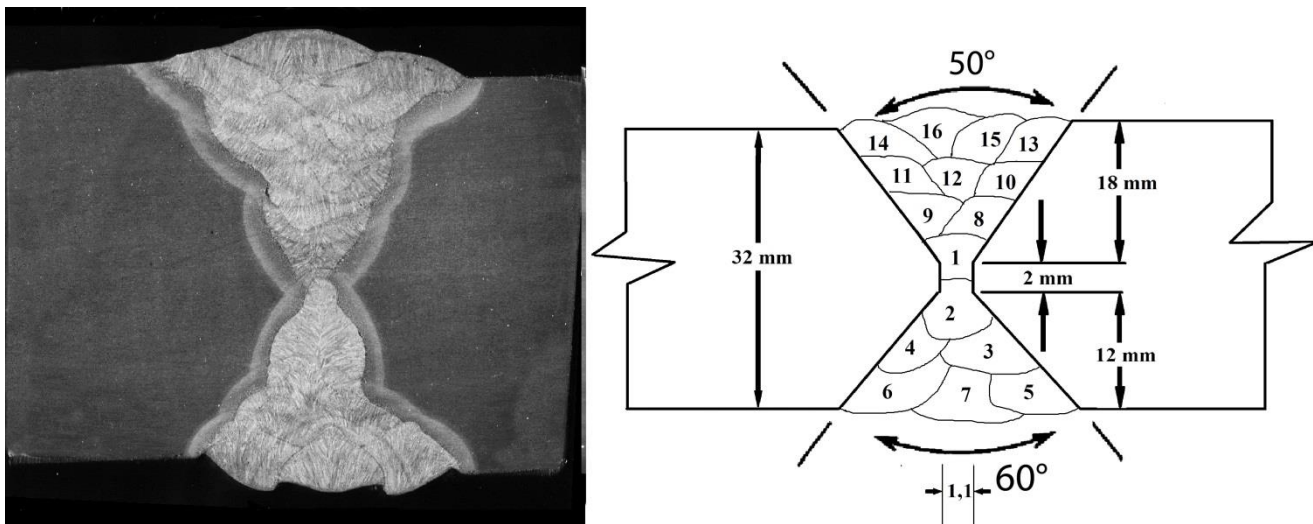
Macrofotografia e esquema dos passes de soldagem utilizados na soldagem dos Chanfros duplo V utilizando um arame tubular com alma metálica.
